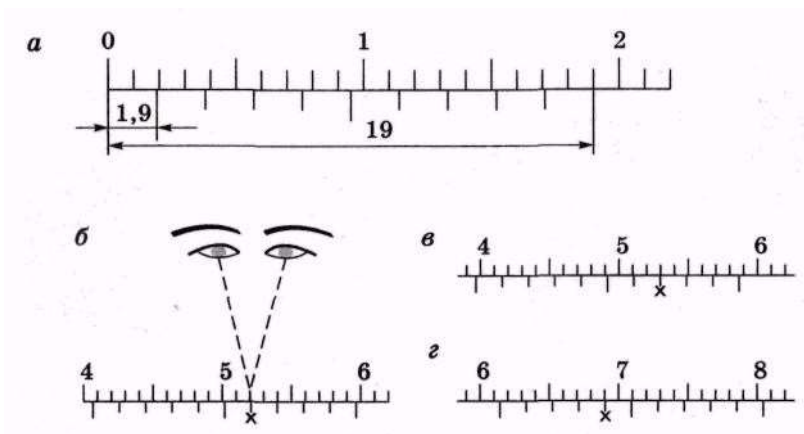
Устройство нониуса (а) и снятие показаний штангенциркуля
